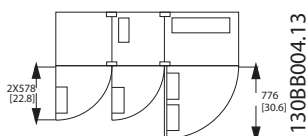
Пространство перед корпусом типа IP21/IP54, типоразмер F3.
